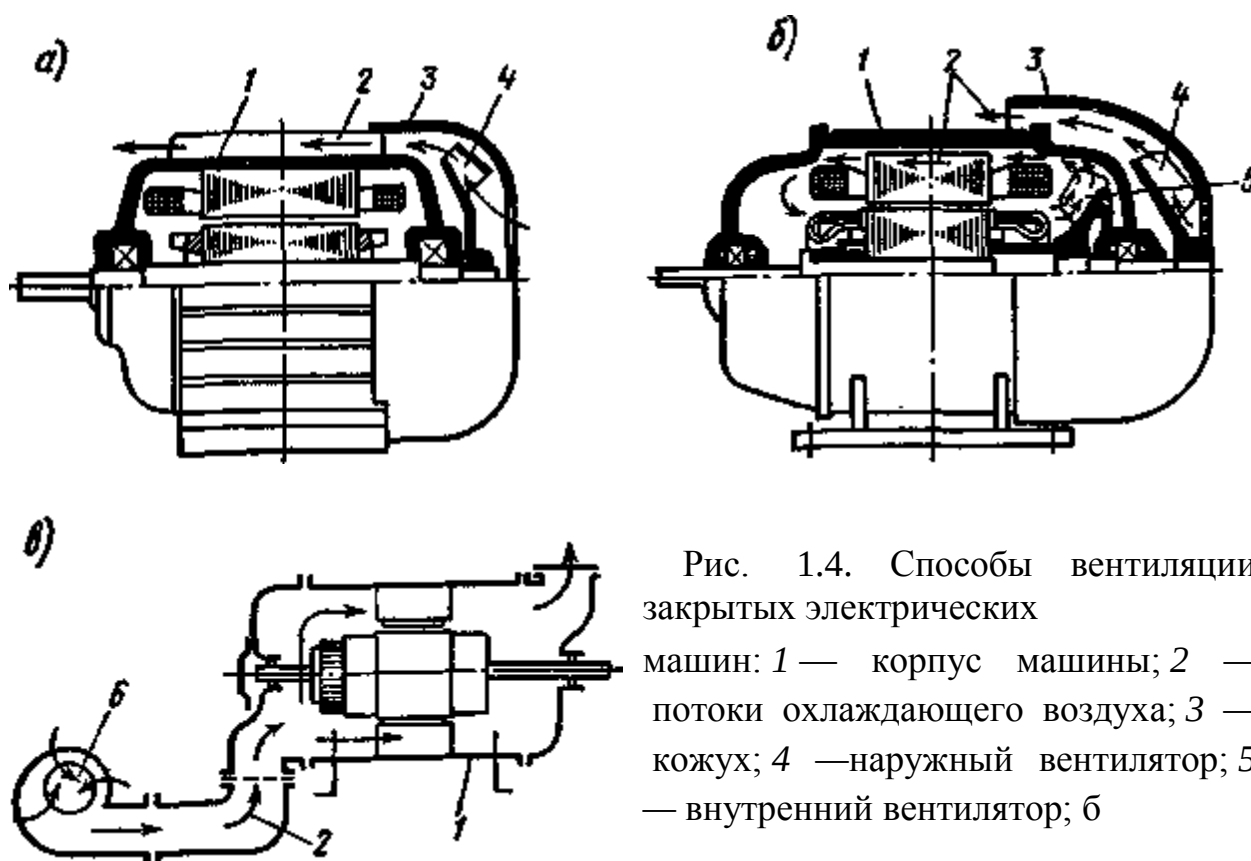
Способы вентиляции закрытых электрических машин: 1 — корпус машины; 2 — потоки охлаждающего воздуха; 3 — кожух; 4 — наружный вентилятор; 5 — внутренний вентилятор; 6 — независимая вентиляция
